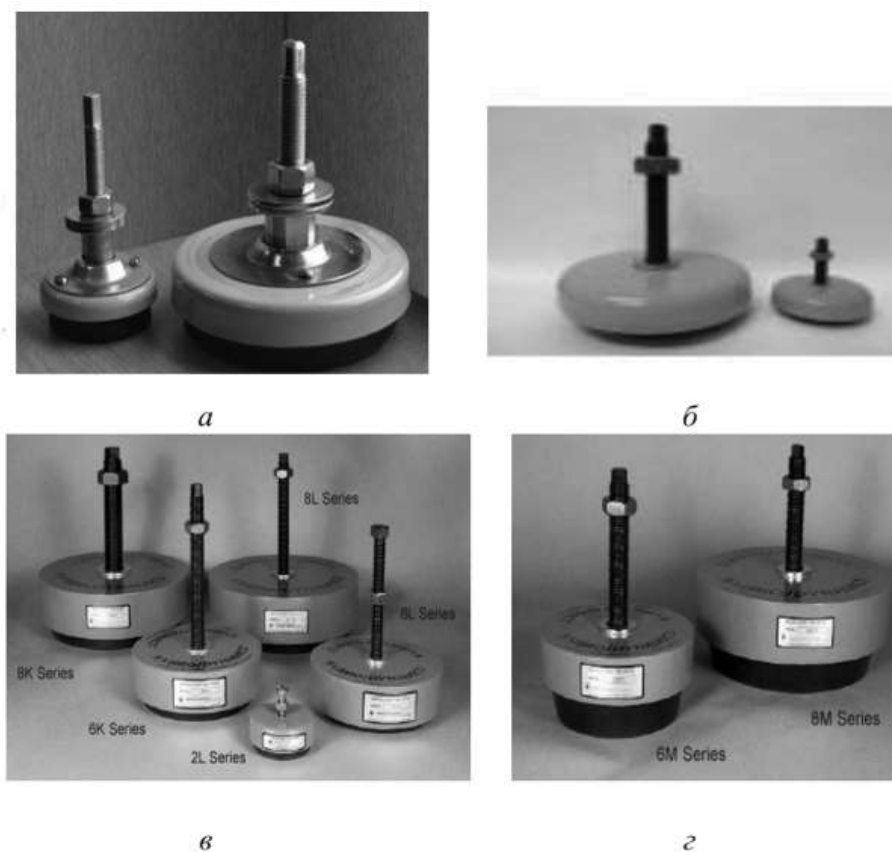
Віброізолюючі опори верстатів: а,б – гумово-металеві; в – підвищеної піддатливості, пневматичних серій «L» і «K»; г – для координатно-вимірювальних машин і шліфувального обладнання
